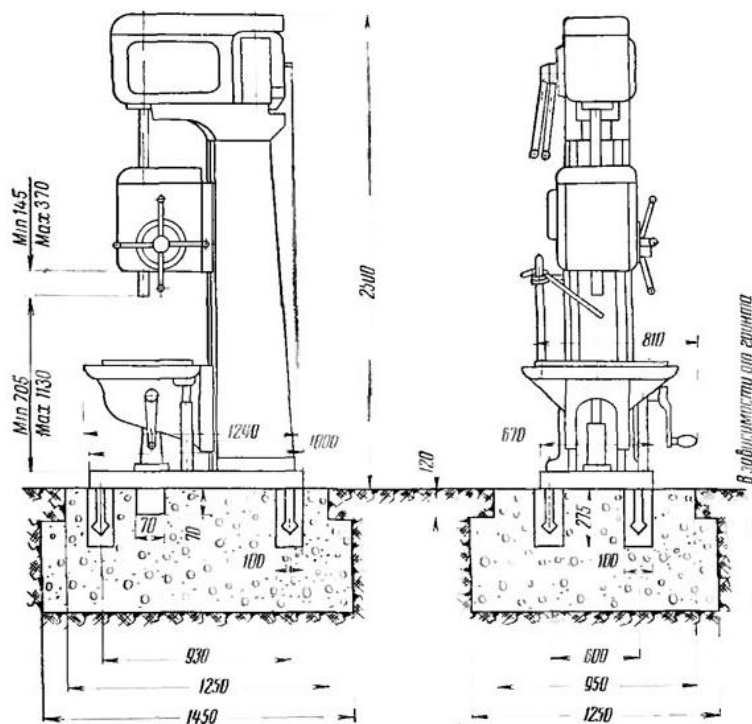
Схема станка 2А135 с габаритными размерами
